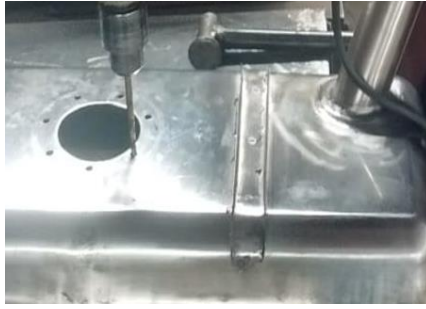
Soldadura de la toma de llenado sobre el molde superior
